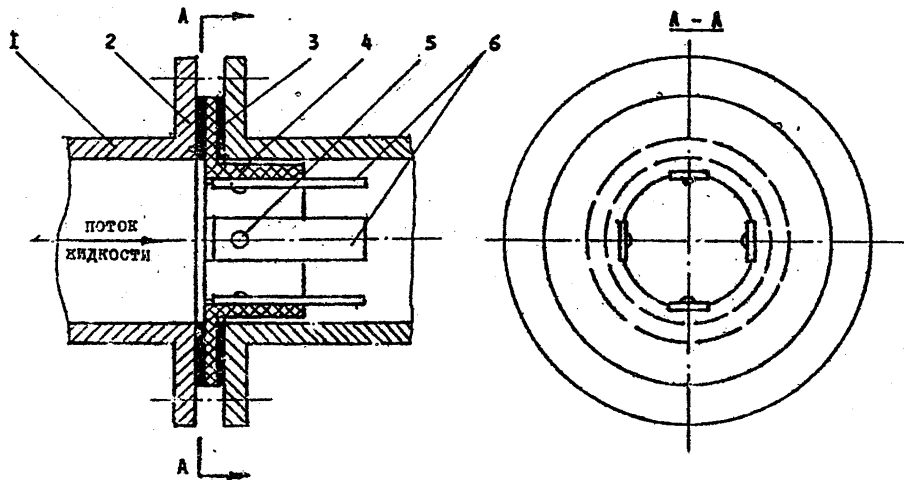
Схема установки цилиндрического пластмассового устройства с образцами-свидетелями в трубопровод при фланцевом соединении.
